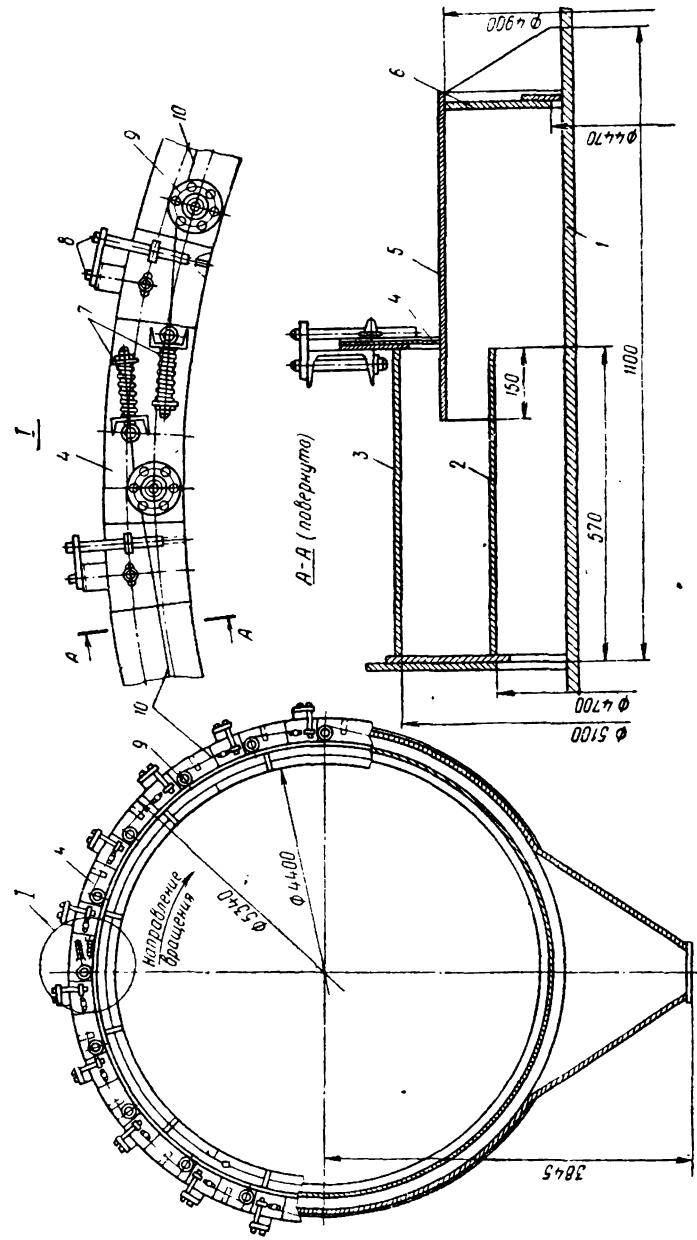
Уплотнительное устройство разгрузочного конца вращающейся печи размером 4,5×170 м:
